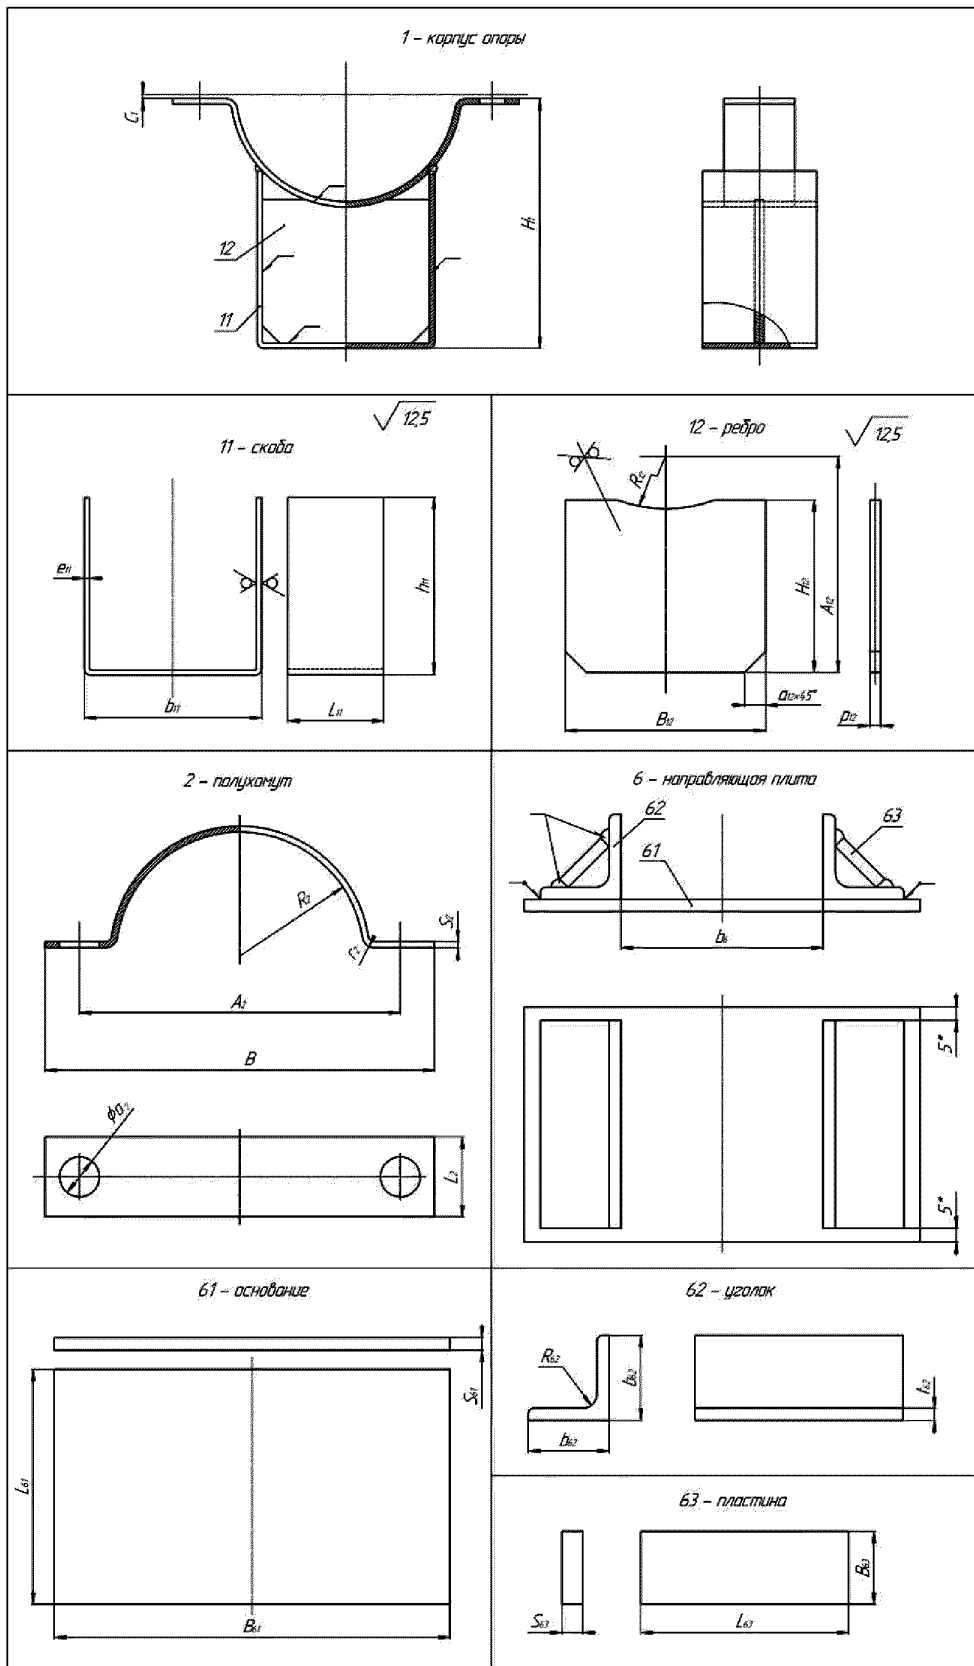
Детали изделий 01-XXXX-G-1C-03-A,
